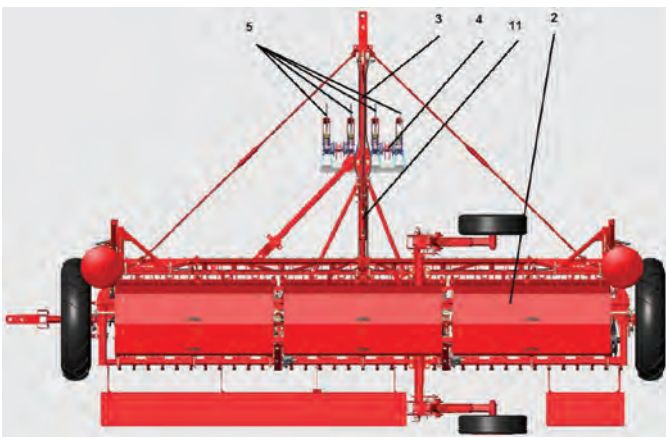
Загальний вигляд системи Броварця на машинно-тракторному агрегаті (вид зверху)
